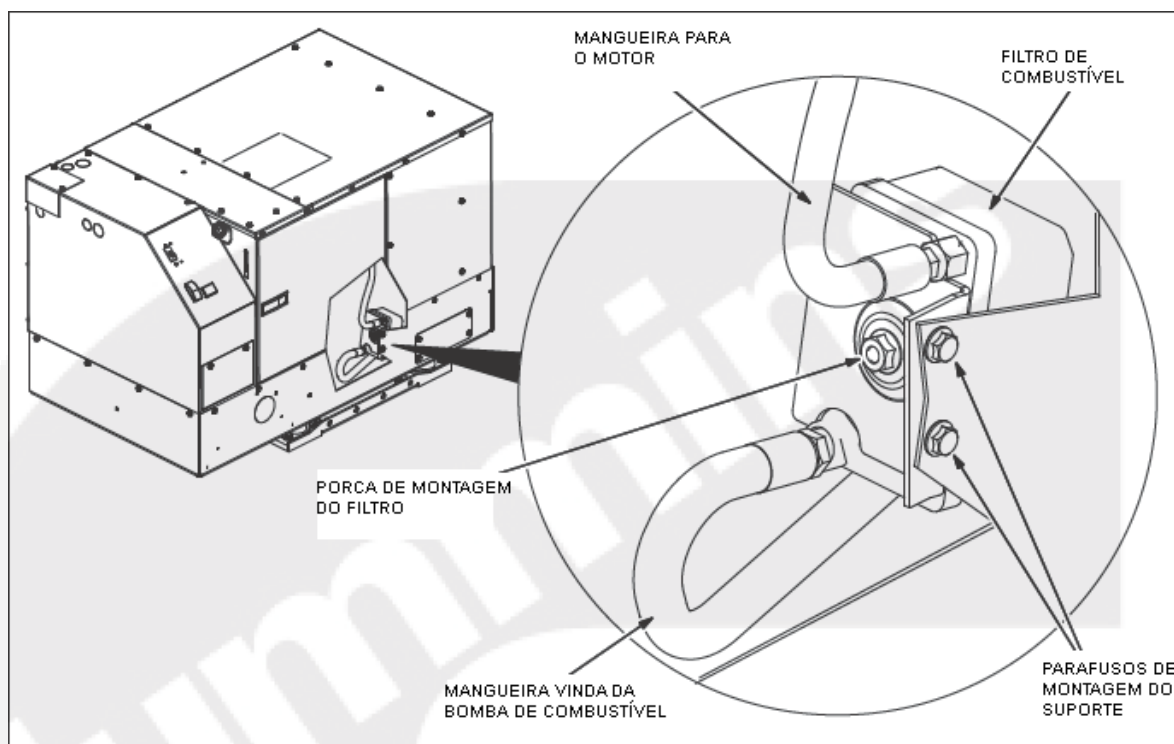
FILTRO DE COMBUSTÍVEL
